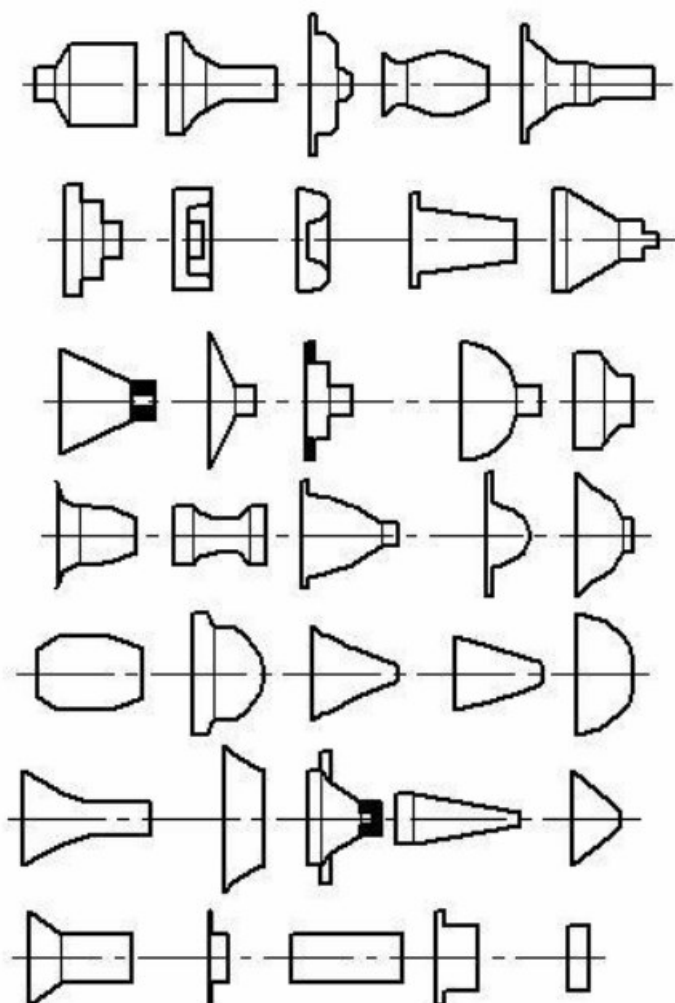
Деталі, що виготовляються ротаційної витяжкою
